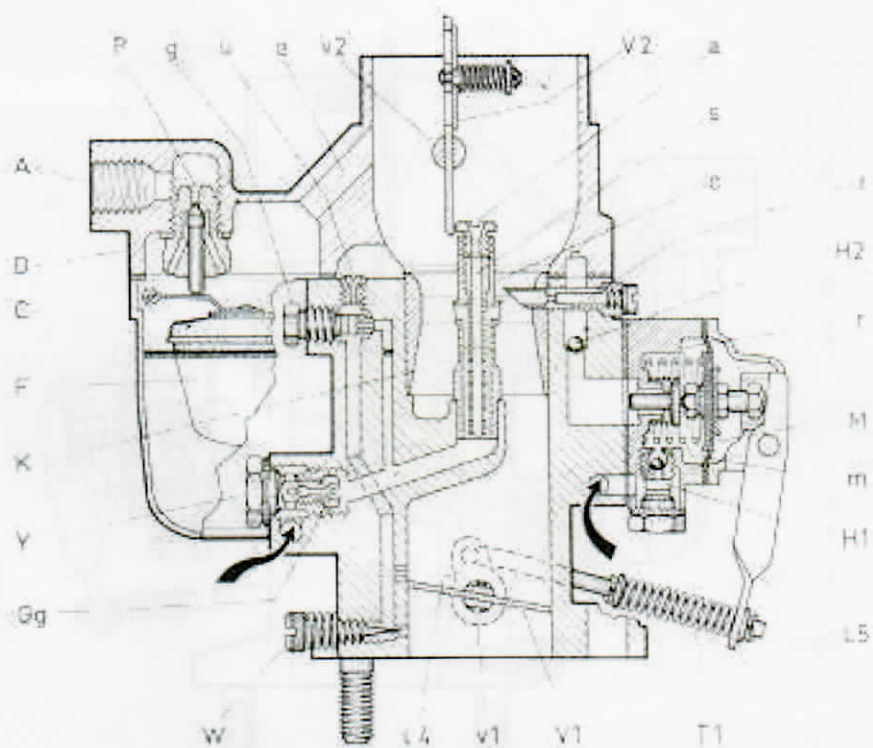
Schem. Schnitt des 32 PCI (3) Glas 600 und 700 Steyr Puch 500 DL E 14838/39 — 14785
